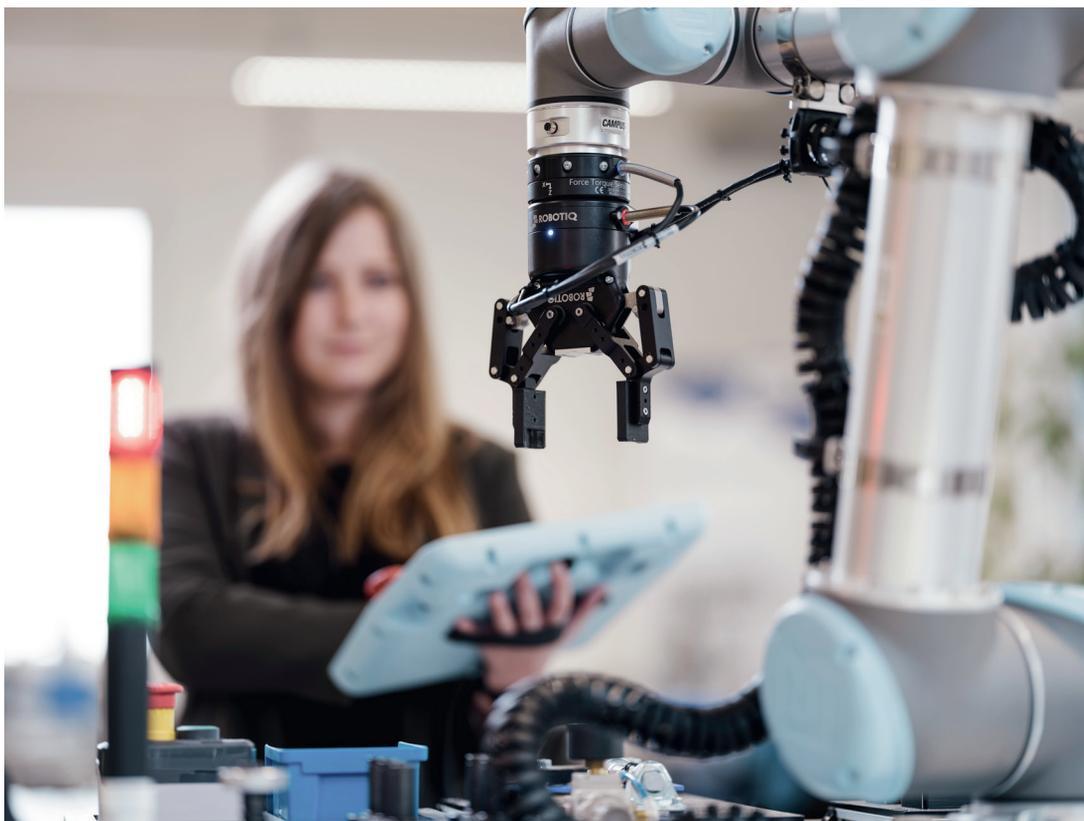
Kollaborativer Roboter im Mechanical Engineering and Robotics Lab.
